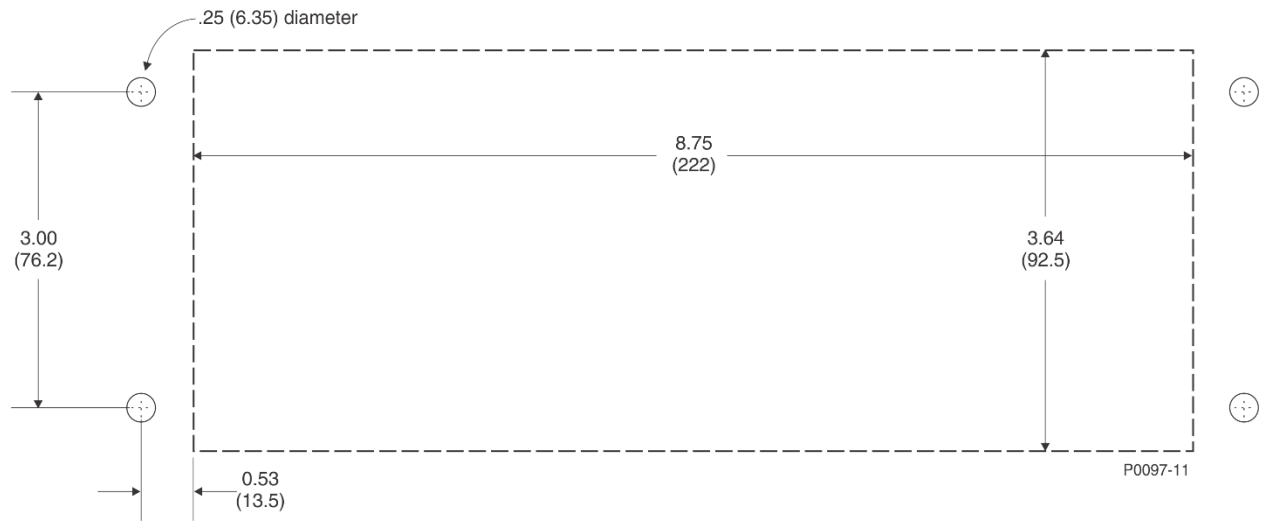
Dimensions de perçage et de découpe d'un BE1-11g H1 simple (boîtier de type P) pour montage sur panneau
